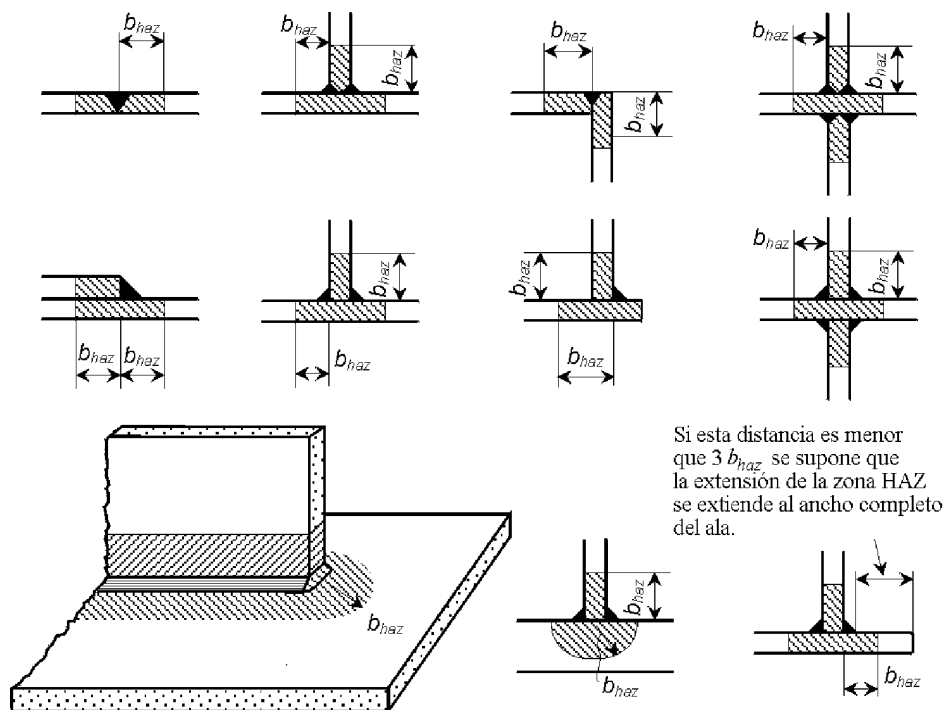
Extensión de las zonas afectadas térmicamente (HAZ)
